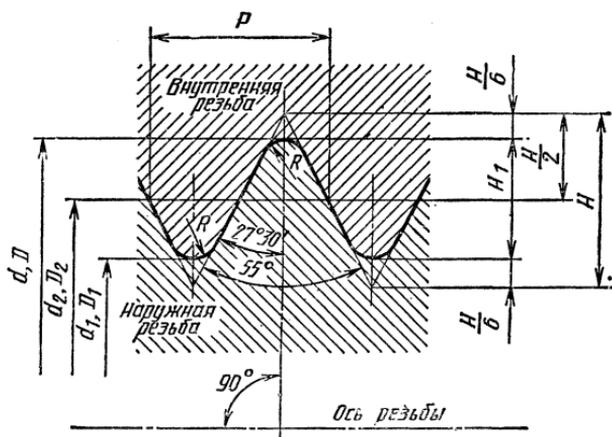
Основные элементы трубной цилиндрической резьбы (ГОСТ 6357—81):
